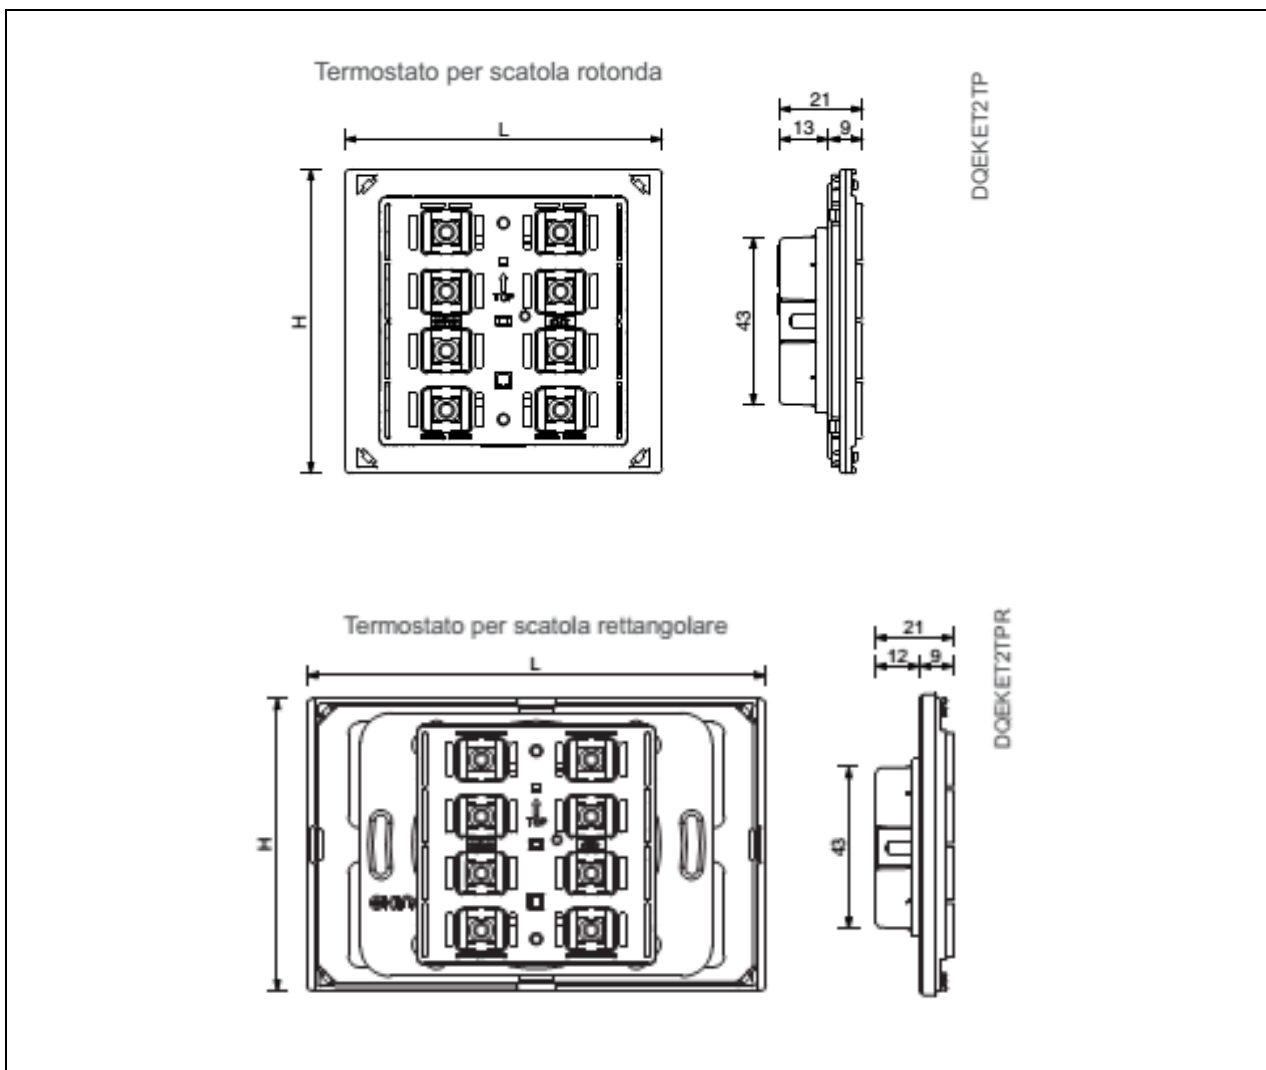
Esecuzione dell'apparecchio: vista frontale e laterale
